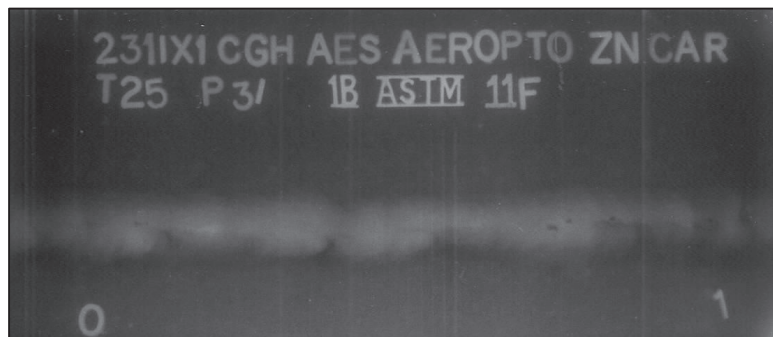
Placa Radiográfica de una Soldadura.
